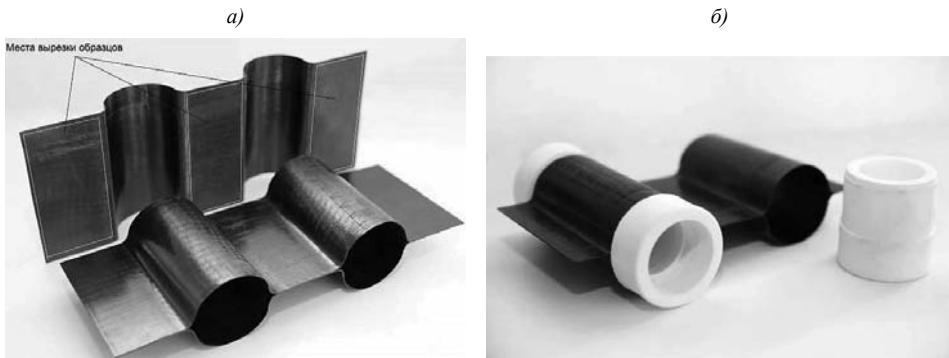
Конструктивно-подобные элементы системы кондиционирования воздуха из листового композиционного термопластичного материала марки ВКУ-44, изготовленные методами: сварки (а) и склеивания (б)
